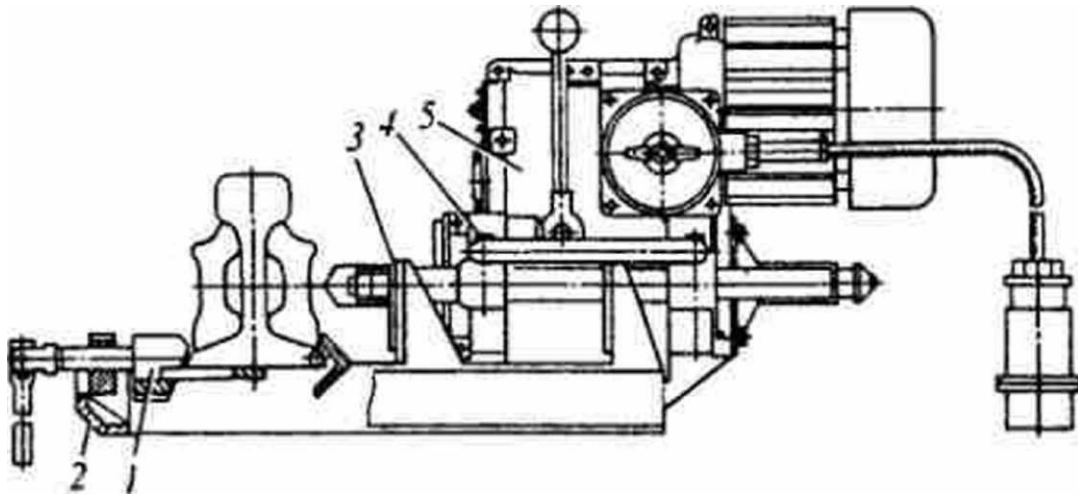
Станок рельсосверлильный РСМ 1М
